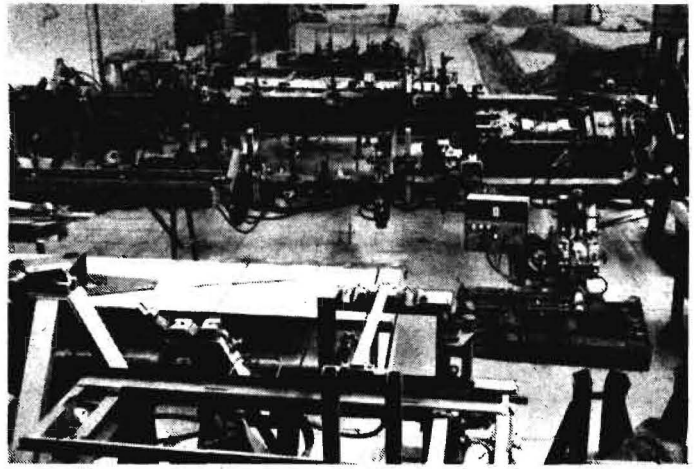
Großschweißvorrichtung für den Preßkanal der Hochdruckpresse K 453
